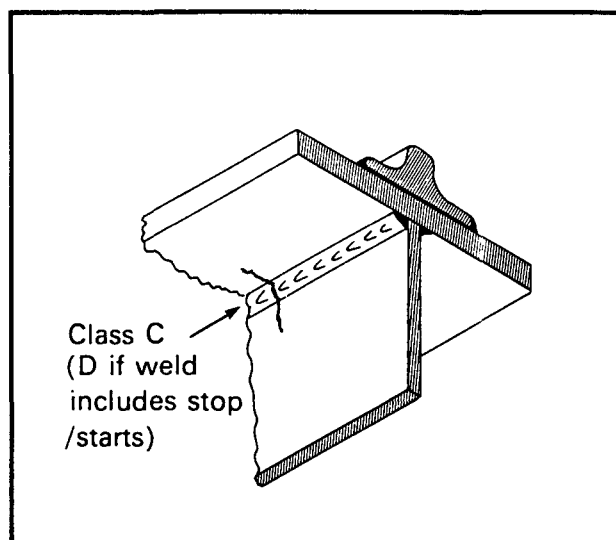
Influence d'une reprise de soudure sur la qualité de l'assemblage [2]
